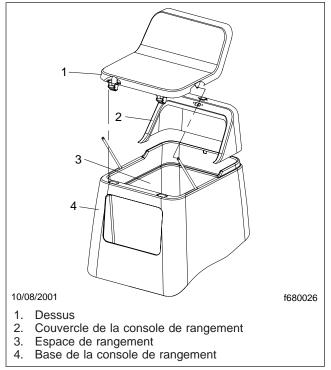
, Console de rangement centrale (avec surface d'écriture)
